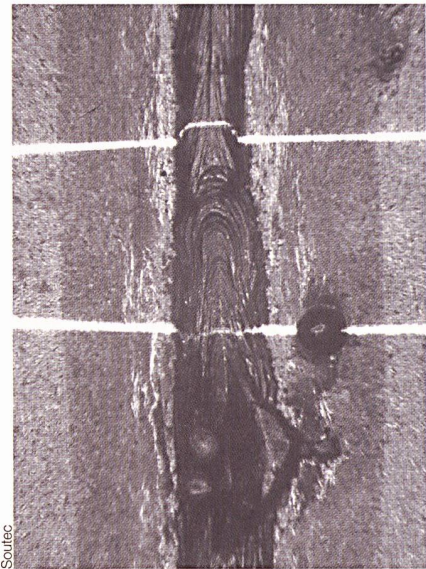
Texturanalyse an einer Schweißnaht.
